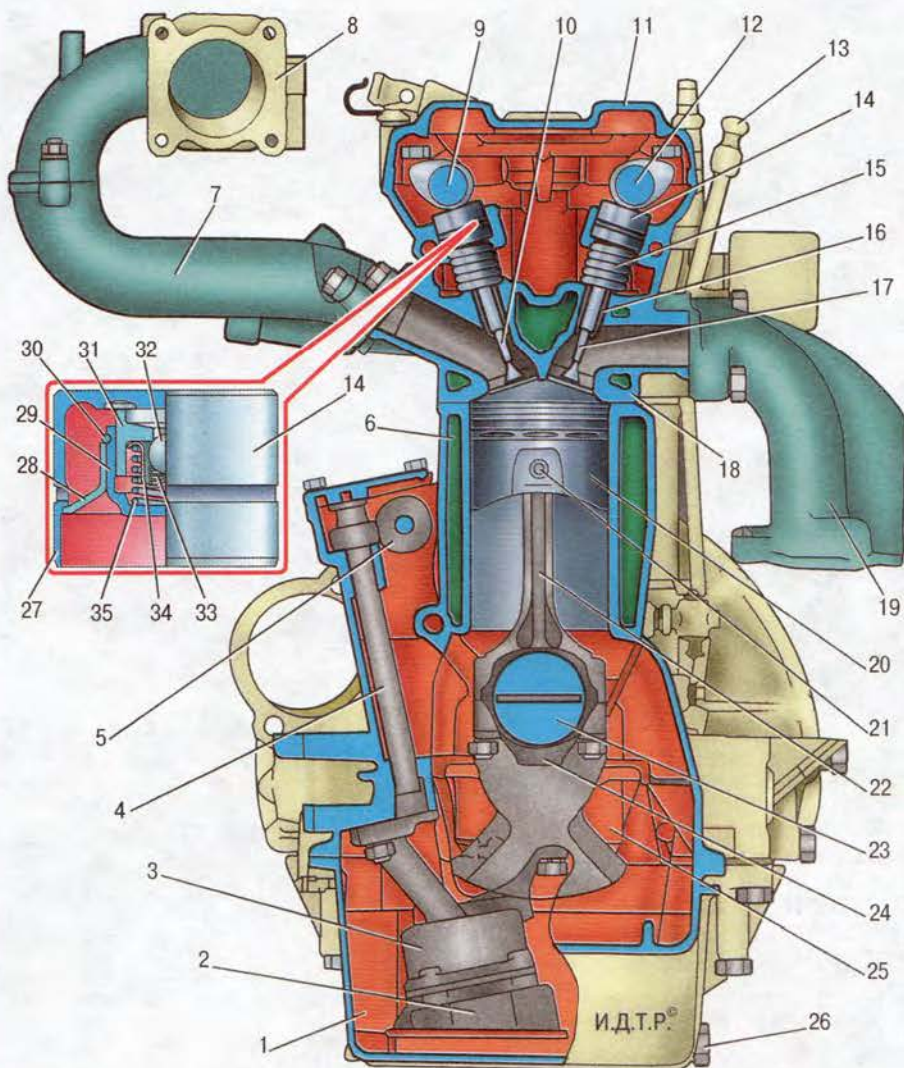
Поперечный разрез двигателя ЗМЗ-409: 1 – масляный картер; 2 – приемник масляного насоса; 3 – масляный насос; 4 – привод масляного насоса; 5 – шестерня промежуточного вала; 6 – блок цилиндров; 7 – впускная труба; 8 – ресивер; 9 – распределительный вал впускных клапанов; 10 – впускной клапан; 11 – крышка клапанов; 12 – распределительный вал выпускных клапанов; 13 – указатель (щуп) уровня масла; 14 – гидротолкатель клапана; 15 – наружная пружина клапана; 16 – направляющая втулка клапана; 17 – выпускной клапан; 18 – головка блока цилиндров; 19 – выпускной коллектор; 20 – поршень; 21 – поршневой палец; 22 – шатун; 23 – коленчатый вал; 24 – крышка шатуна; 25 – крышка коренного подшипника; 26 – пробка сливного отверстия; 27 – корпус толкателя; 28 – направляющая втулка; 29 – корпус гидротолкателя; 30 – стопорное кольцо; 31 – поршень гидротолкателя; 32 – шариковый клапан; 33 – пружина шарикового клапана; 34 – корпус шарикового клапана; 35 – разжимная пружина
